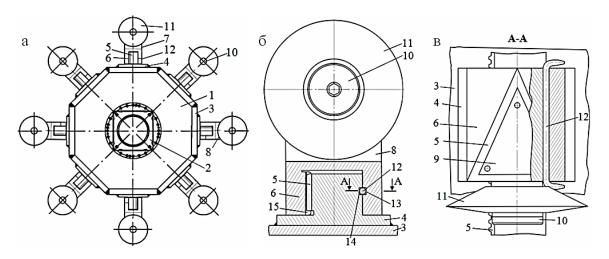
Рабочий орган с дисковым инструментом: a — общий вид; b — зубчато-реечный замок трехгранной призмы; b — зона размещения проволочного фиксатора
